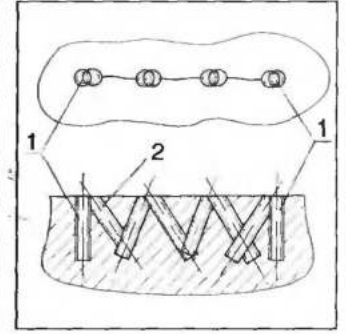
Ремонт трещины с помощью резьбовых штифтов: 1 — штифты, устанавливаемые в края трещины; 2 — штифты, устанавливаемые с перекрытием
